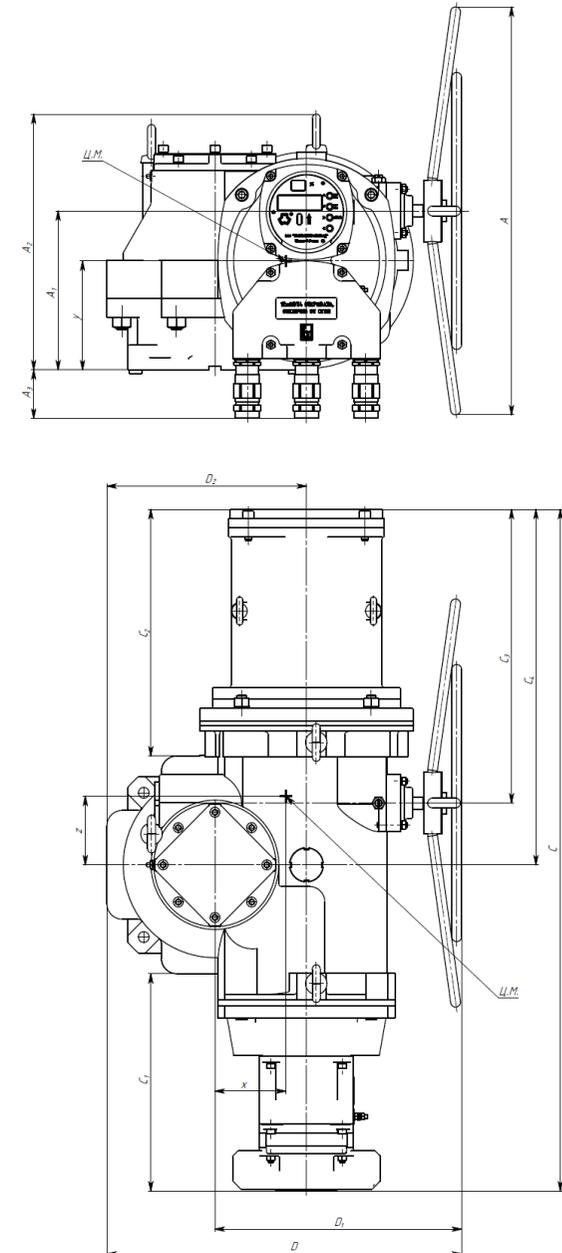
г – Габаритные размеры привода конструктивной схемы 43
